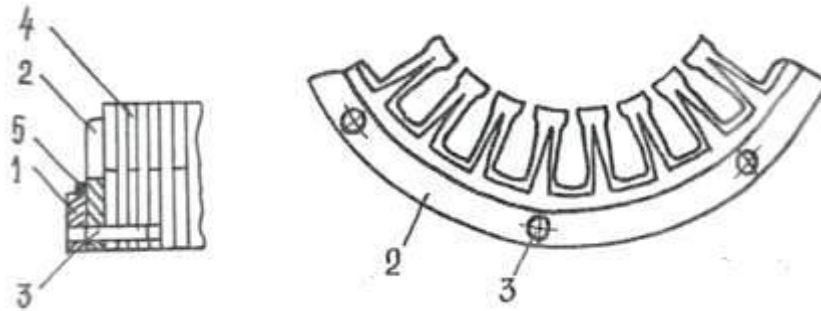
Відновлення пакету статора шляхом встановлення додаткових шайб: 1 – основна натискна шайба; 2 – додаткова натискна шайба із зубцями; 3 – фіксуєчий штифт; 4 – пластини статора; 5 – зварний шов
